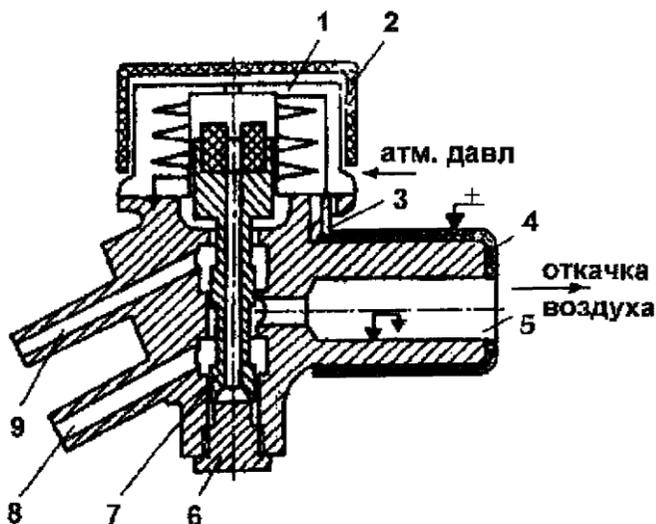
Схема электромагнитного пульсатора для попарного доения: 1 – электромагнит; 2 – кожух; 3 – металлическая оболочка; 4 – прокладка; 5 – патрубок; 6 – пробка; 7 – стержень; 8, 9 – патрубки пульсирующего вакуума.
